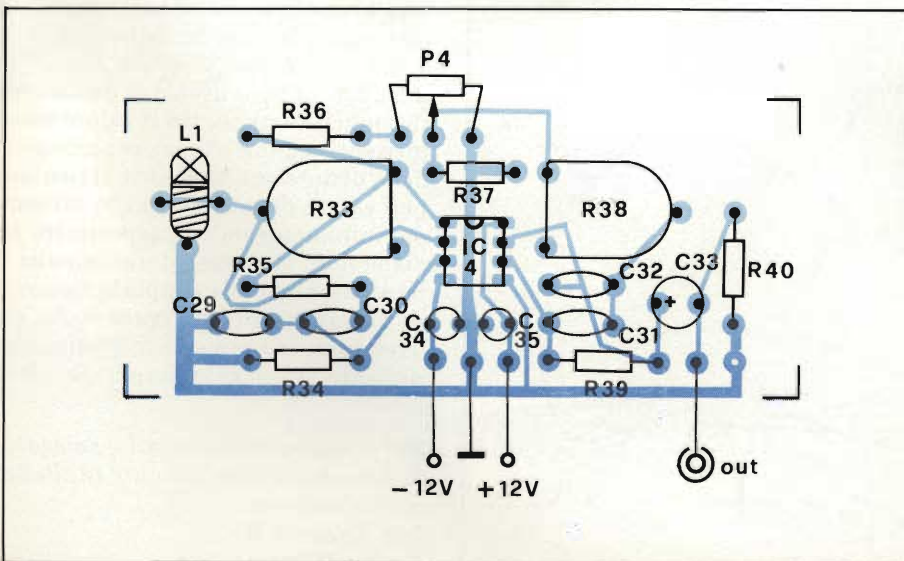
Disposizione componenti dello stampato di fig. 9.
